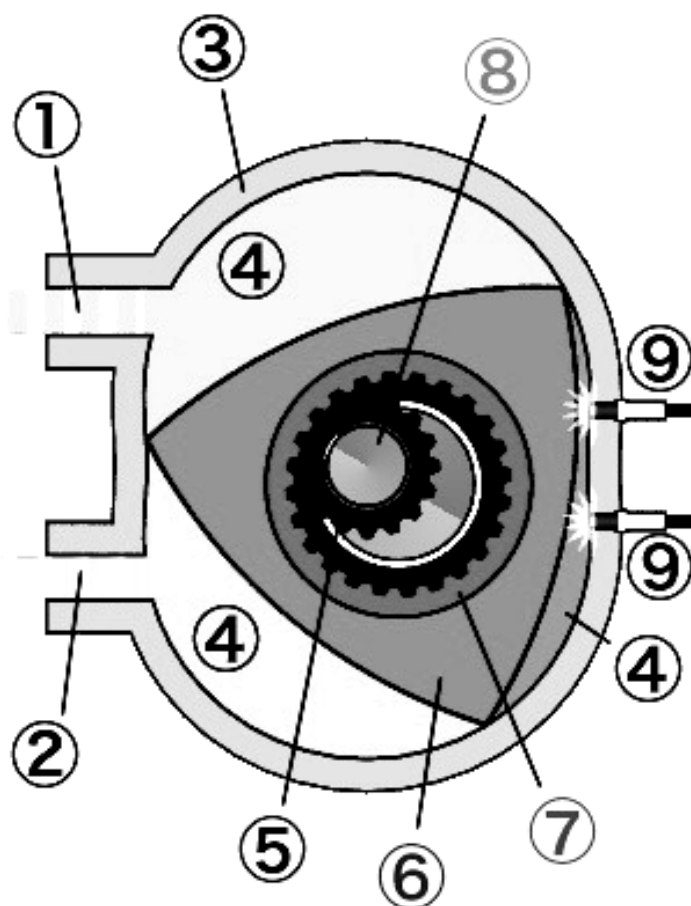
Схема роторно-поршневого двигателя: 1 – впускное окно; 2 – выпускное окно; 3 – корпус; 4 – камера сгорания; 5 – неподвижная шестерня; 6 – ротор; 7 – подвижное зубчатое колесо; 8 – вал; 9 – свеча зажигания
